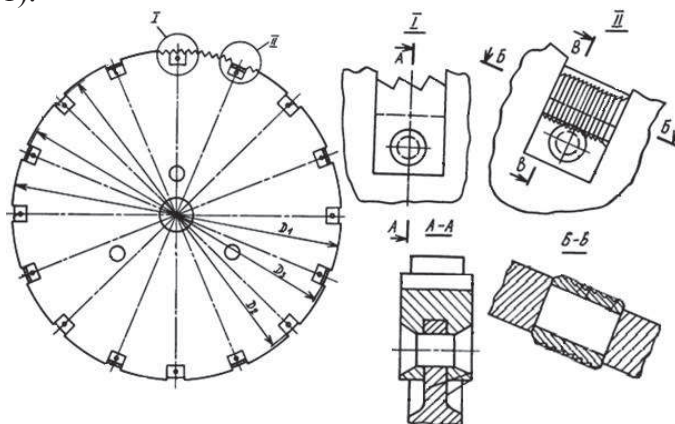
Дисковая пила с сегментами для резки металлоизделий
